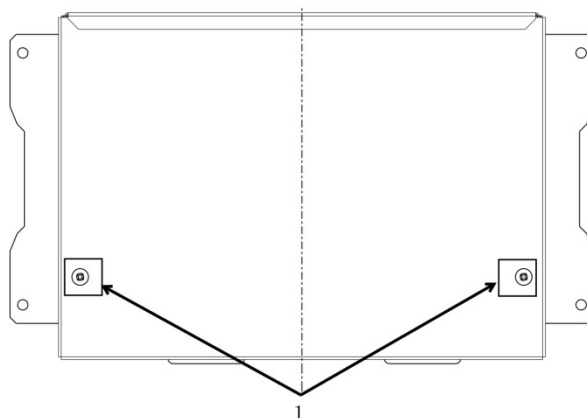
Posición de instalación de la cubierta superior de la caja del amplificador
